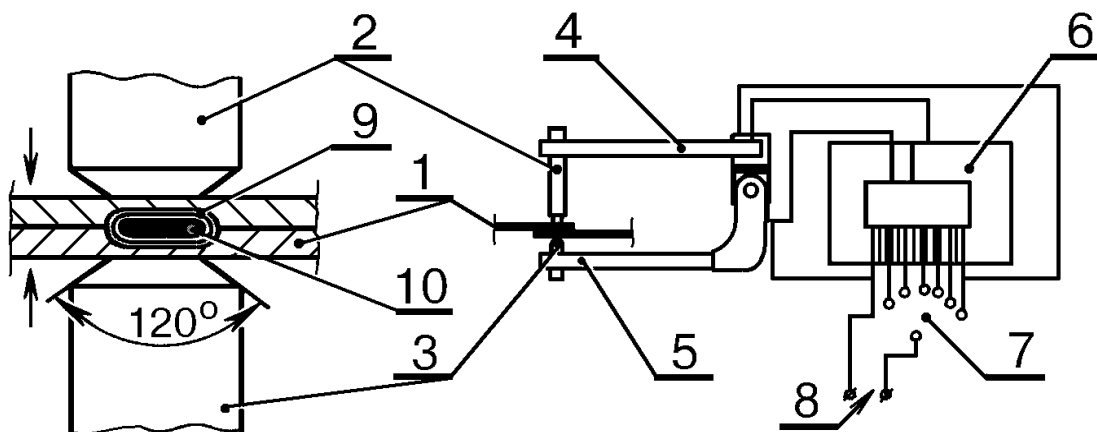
Принципы работы аппарата точечной сварки:
